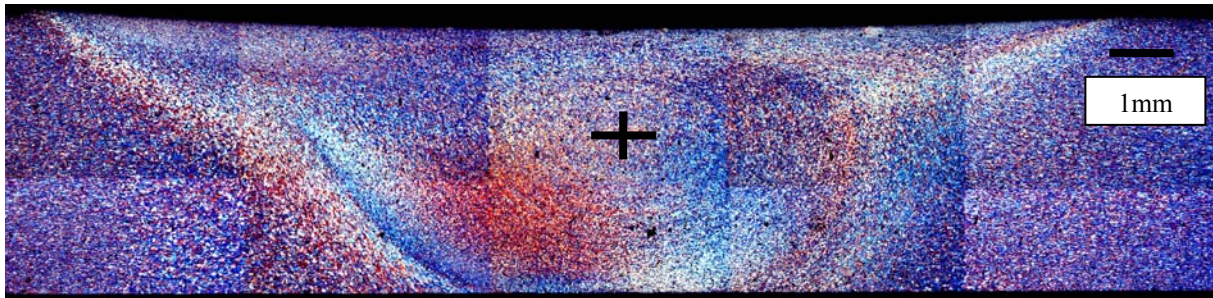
Cartographie d'un joint soudé 5251 H14 après attaque anodique. Microscopie optique
